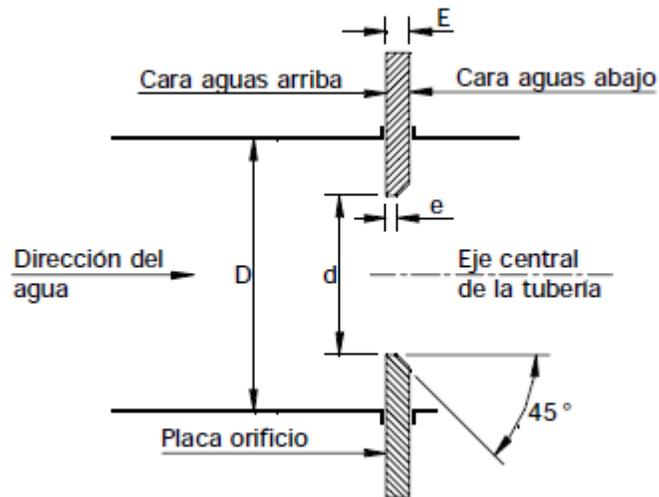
Dimensiones generales de la platina de orificio. Fuente propia.
